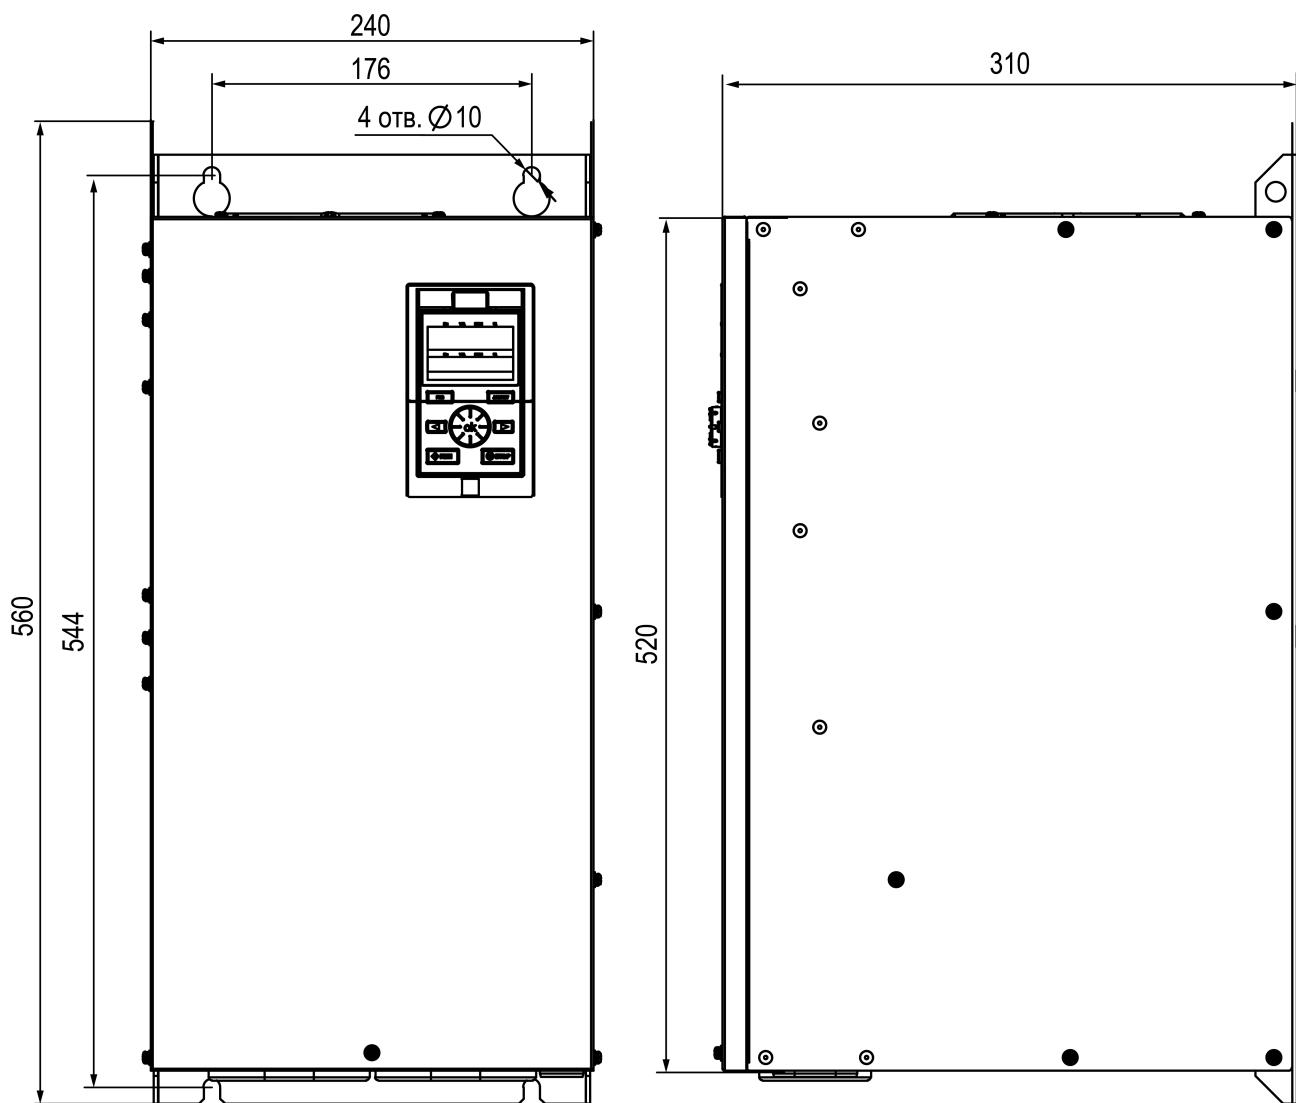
Габаритные размеры прибора в корпусе типоразмера 6
